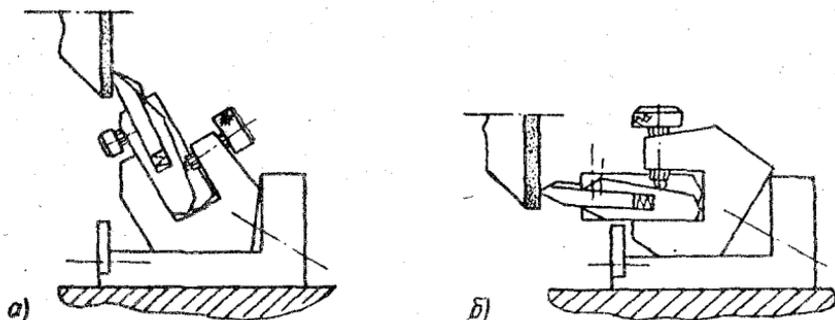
Пакетная заточка резцов с разными углами при вершине: а) заточки по боковым граням; б) заточка по вершинам
